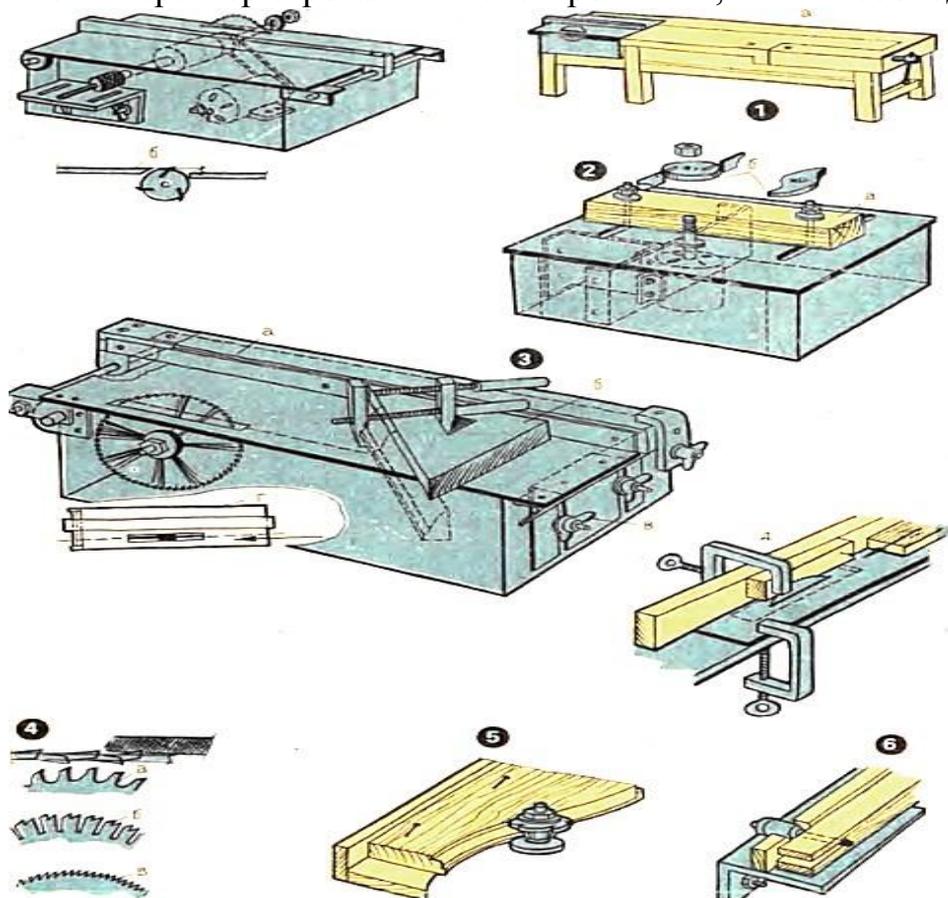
Станки для обработки дерева: 1 - универсальный станок с ножевым пильным валиком и фрезерным патроном: а - станок встроен в верстак; б - подъем за резцовой частью стола рубанка;
